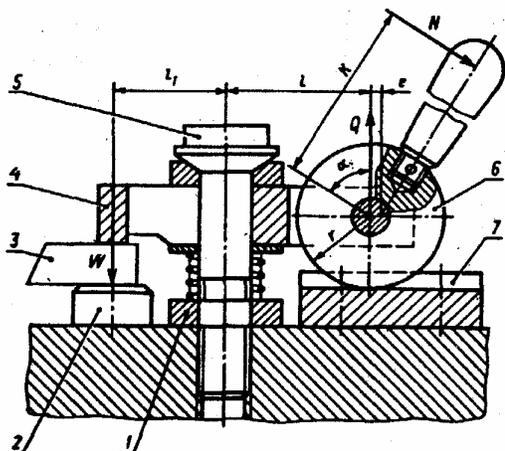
Нормализованный эксцентриковый прихват
